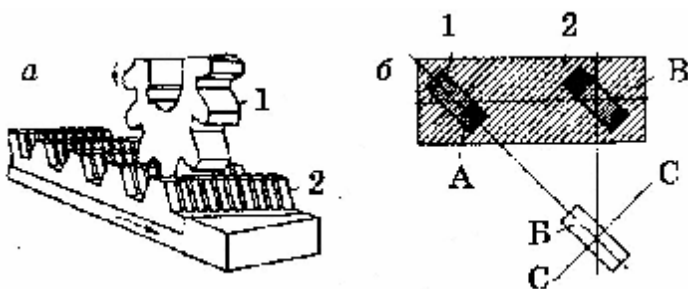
Шевингование шеввер-рейкой и шеввер-червяком: а — шеввер-рейкой; б — схема скольжения шеввер-рейки по зубьям зубчатого колеса
